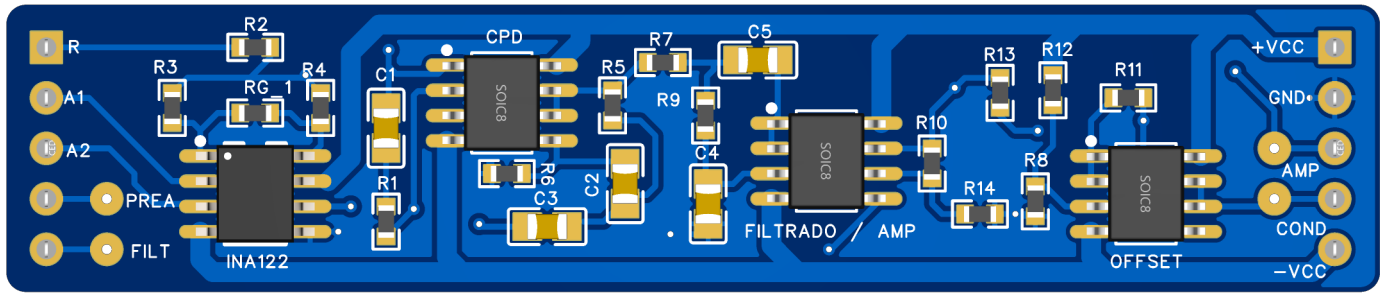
Vista general de la PCB del sistema inalámbrico de adquisición de EGG.
